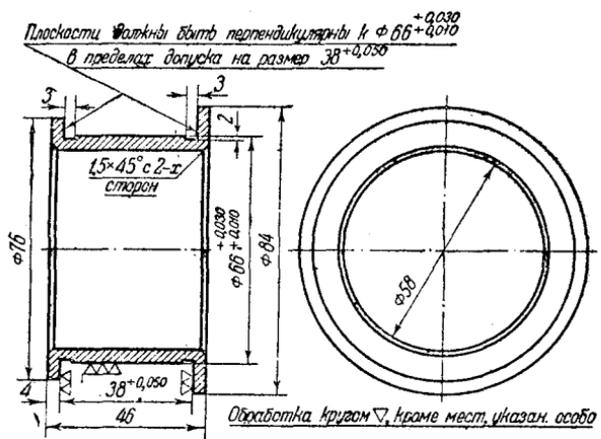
Дет. № 03138. Втулка переднего коренного подшипника
